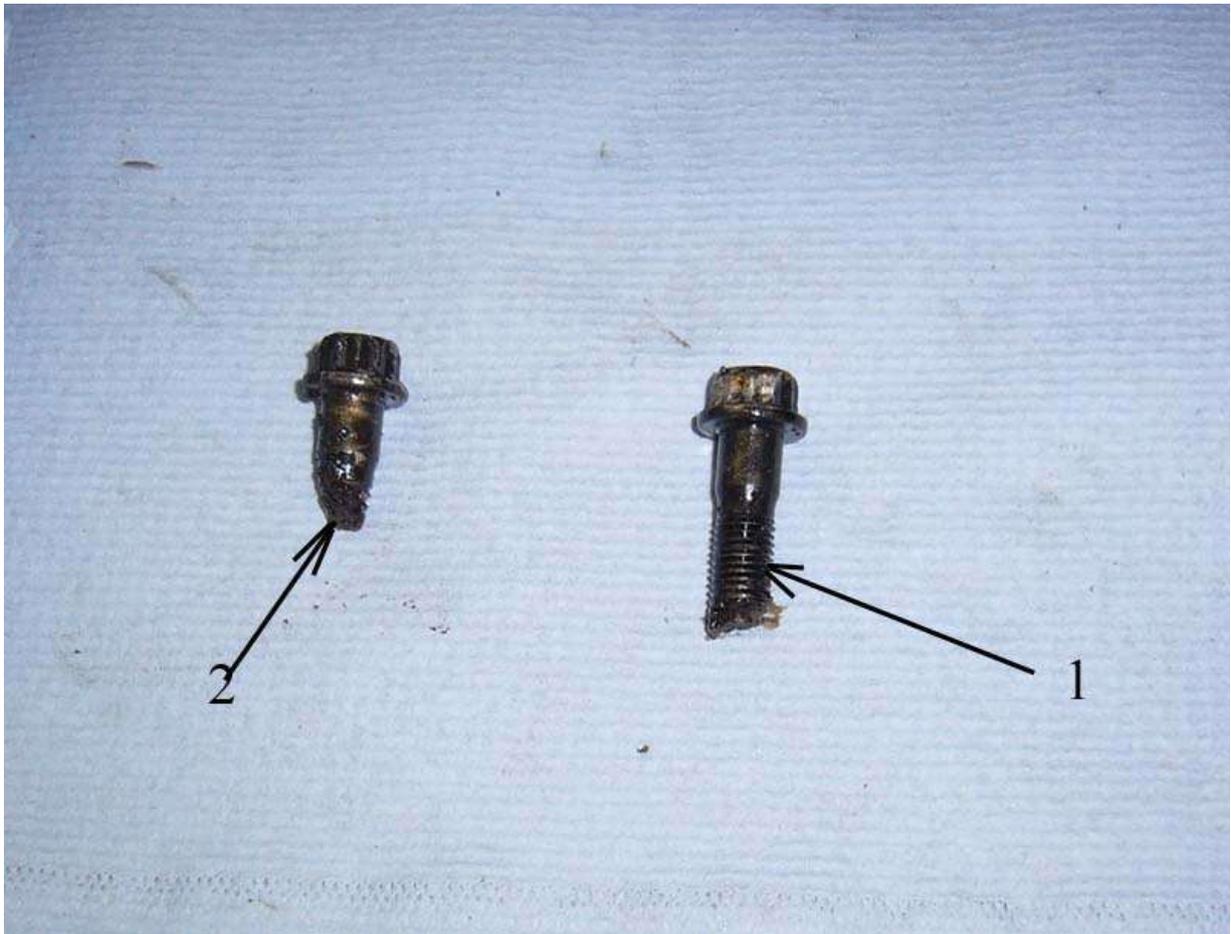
Обломки болтов крепления крышки шатуна 1-го цилиндра.
